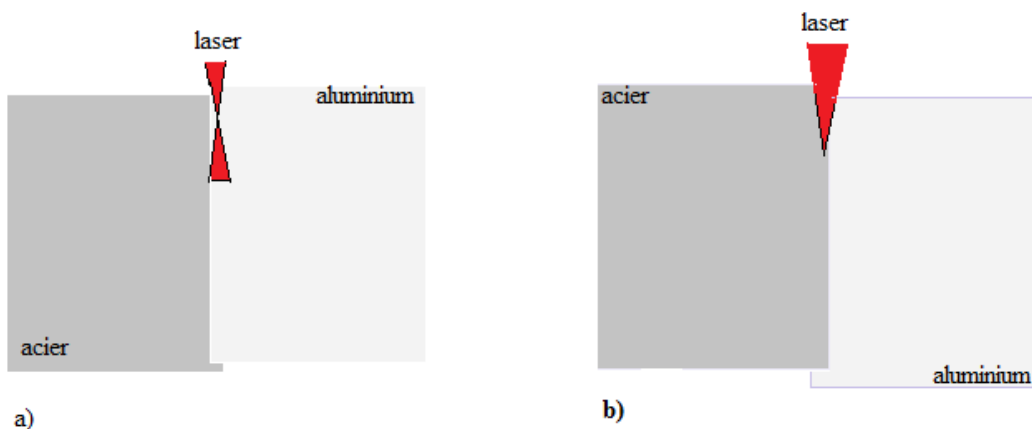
Procédé de soudage par faisceaux laser ; a) laser défocalisé. b) laser focalisé [2].
